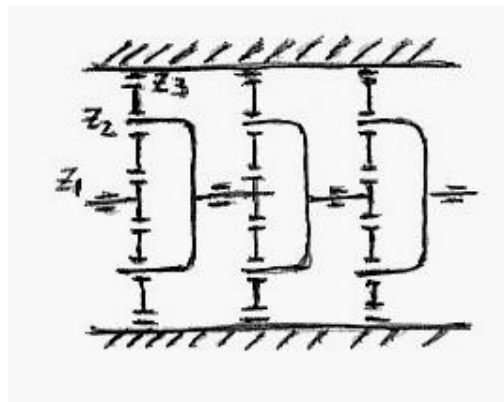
Схема многоступенчатого планетарного редуктора
